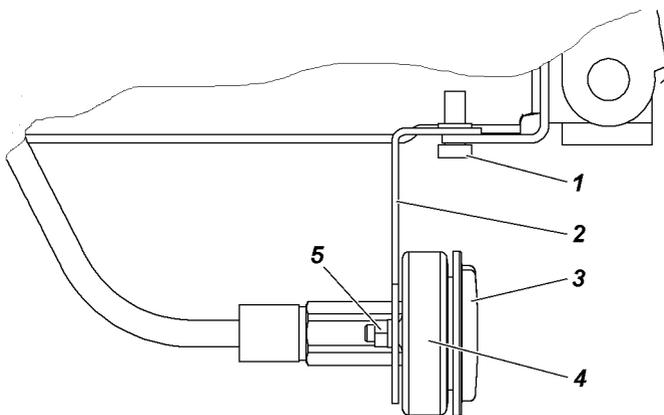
Установка заправочного устройства с поперечным расположением баллона:
